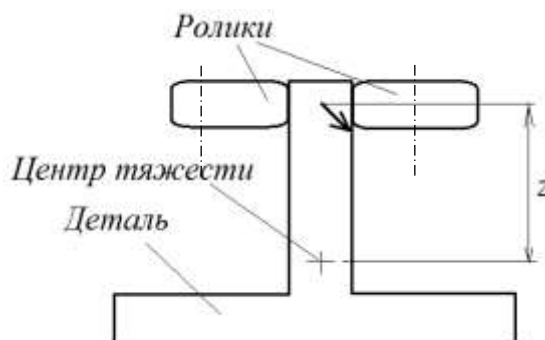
Схема раскатки ребра конструктивно-подобного образца детали
